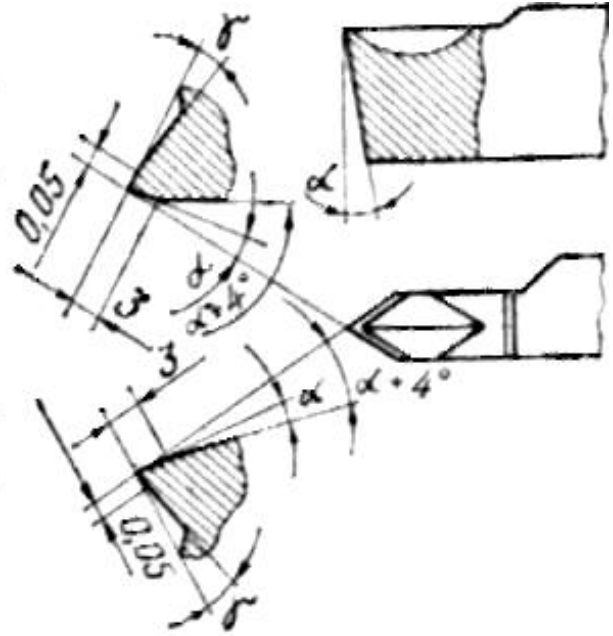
Різьбовий різць з швидкорізальною для обробки важкооброблюваних сталей
